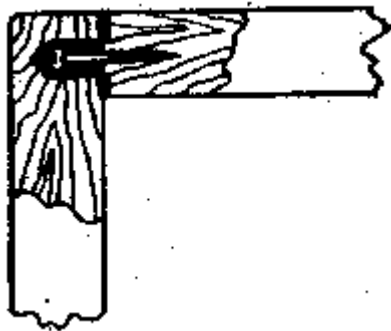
Соединение деталей из древесно-стружечной плиты
